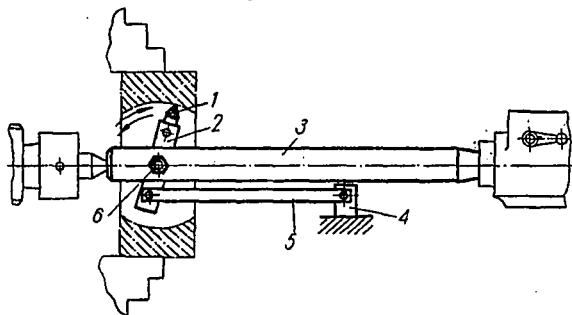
Приспособление с тягой для расточки внутренних сферических поверхностей.
